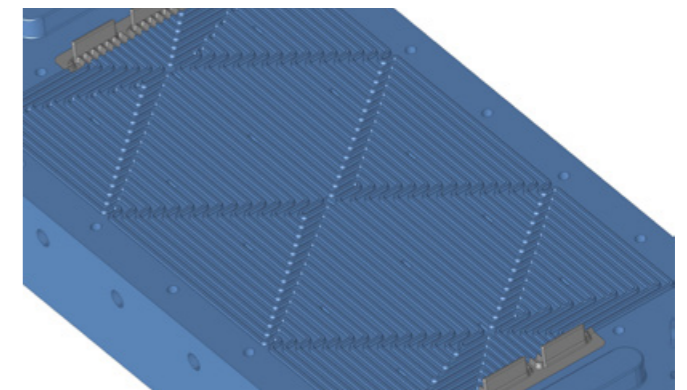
CAD-Modell des Werkzeugeinsatzes
